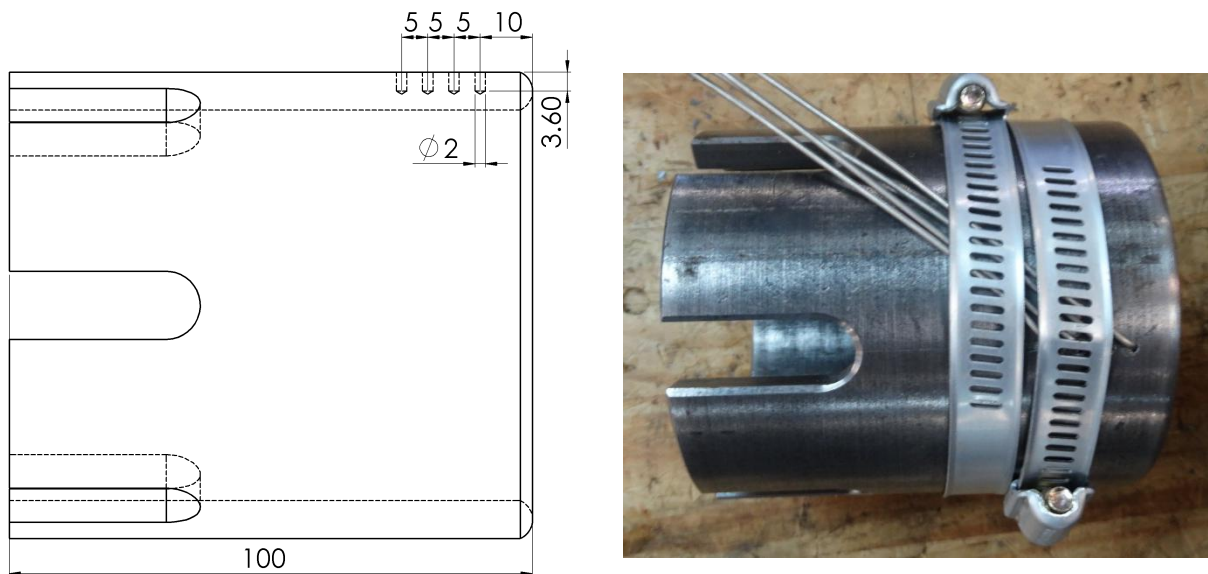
Posição dos termopares e fixação da abraçadeira.
